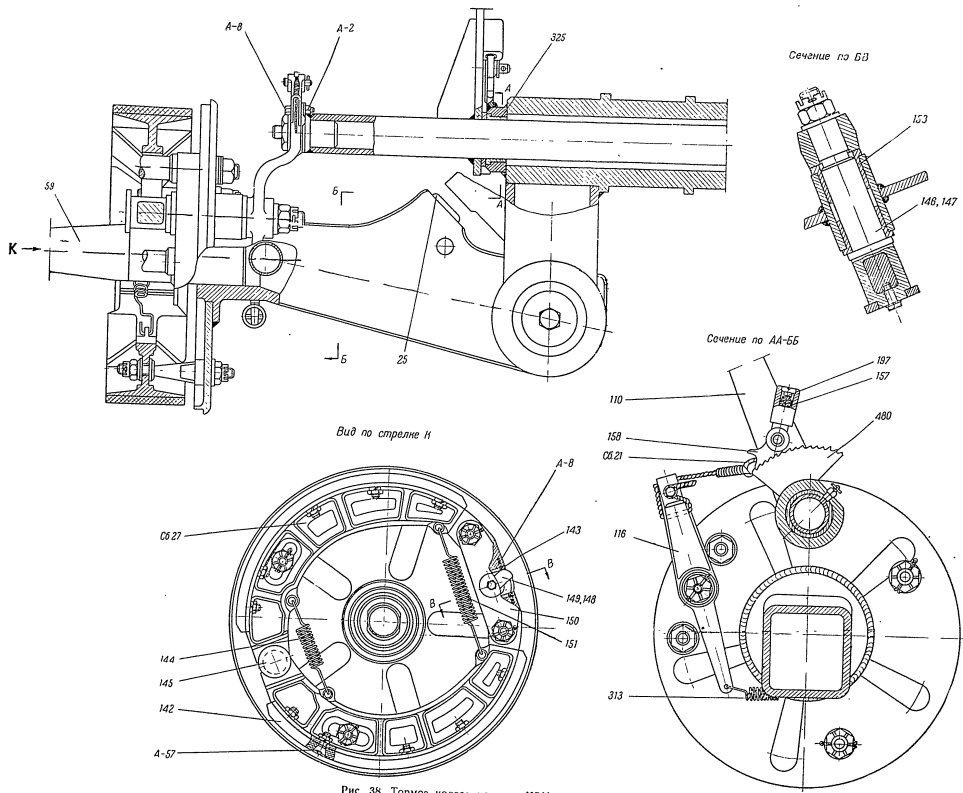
Тормоз колеса повозки КЗУ-16 (сб. 20);
